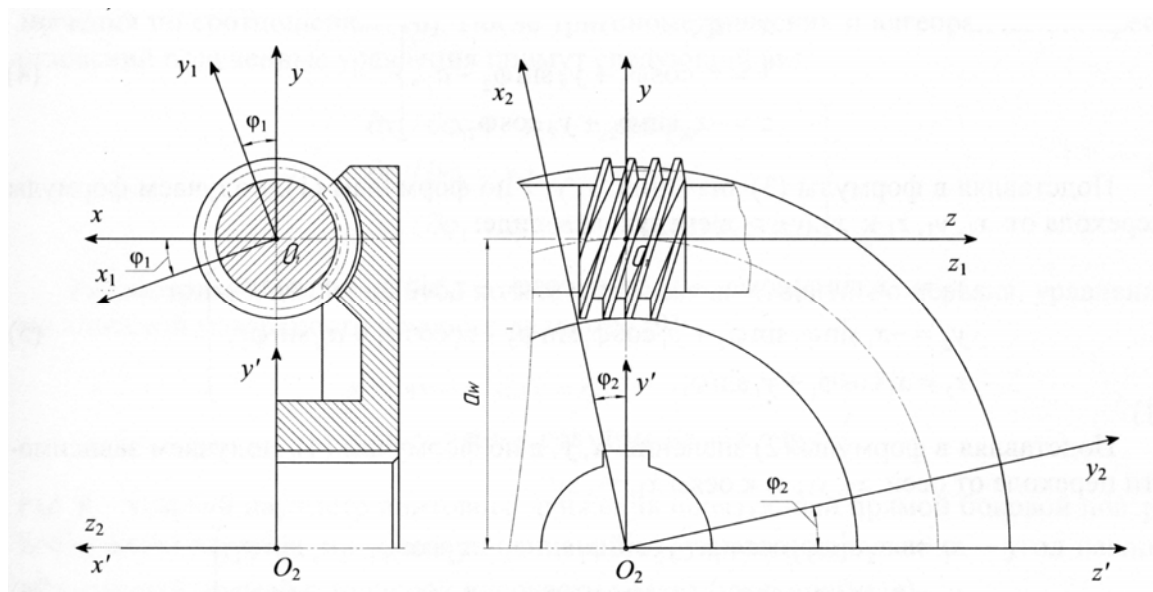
Схема зацепления червяка с зубьями венца колеса двухвенцово́й червячной передачи
